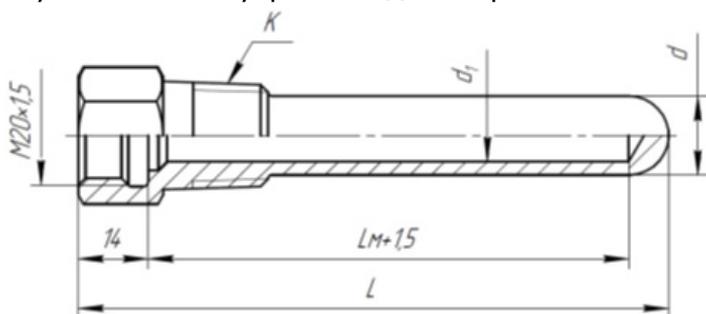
ГТ-712 цилиндрическая с конической резьбой для датчиков с
